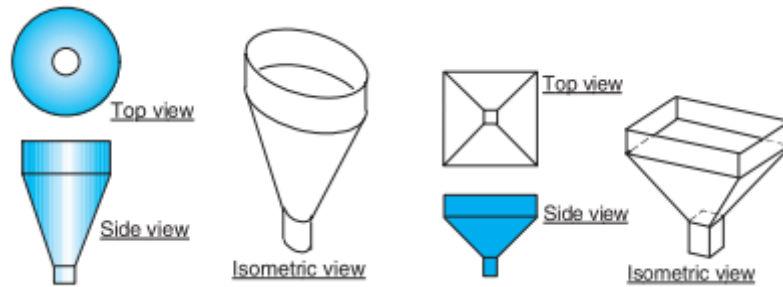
Buen diseño de tolva (izda) y mal diseño de tolva (dcha). Fuente [5]
